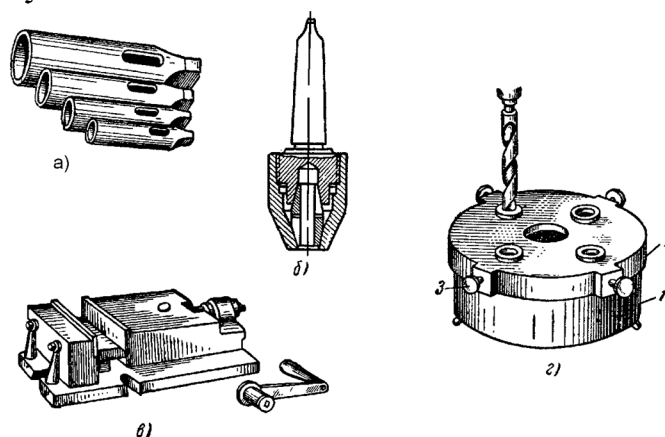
Принадлежности и приспособления к сверлильным станкам:
